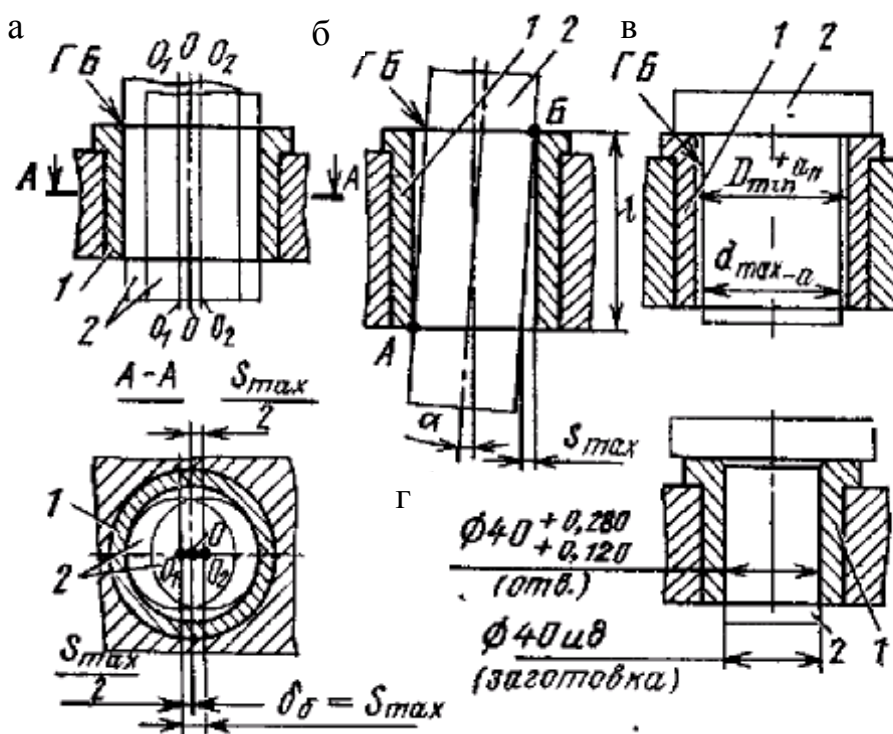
Схема базирования заготовки с главной базой, имеющей форму цилиндрической наружной поверхности, в отверстие.
